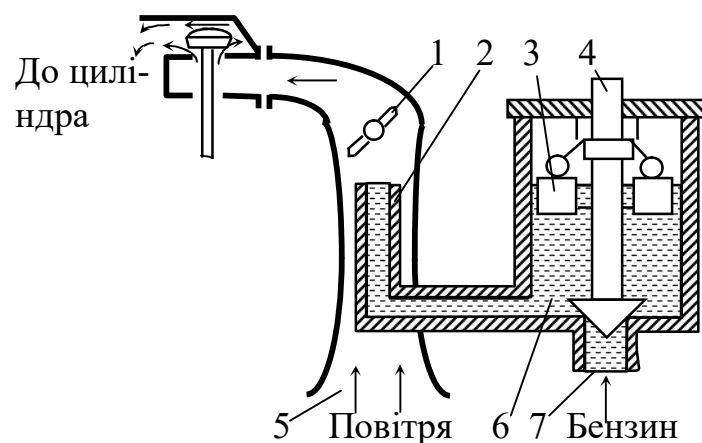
Будова карбюратора: 1 – дросельна заслінка; 2 – трубка подачі палива; 3 – поплавок; 4 – запірна голка; 5 – дифузор; 6 – робоча камера; 7 – отвір для подачі палива
